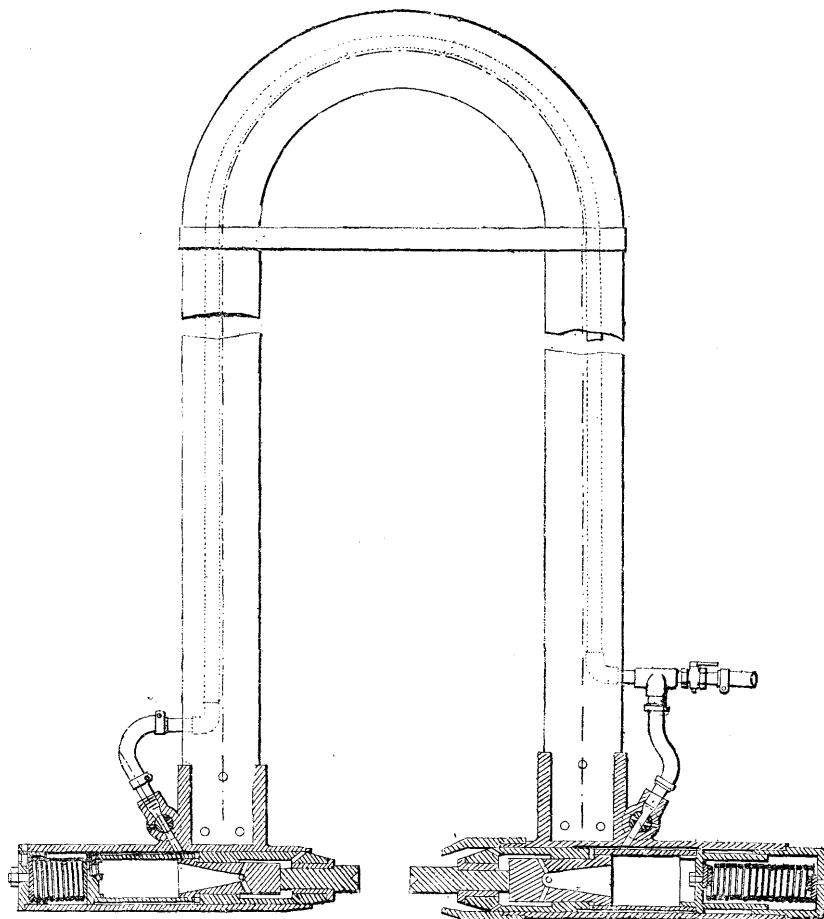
Riveuse à tas mobile de la Q and C Company, de Chicago.
